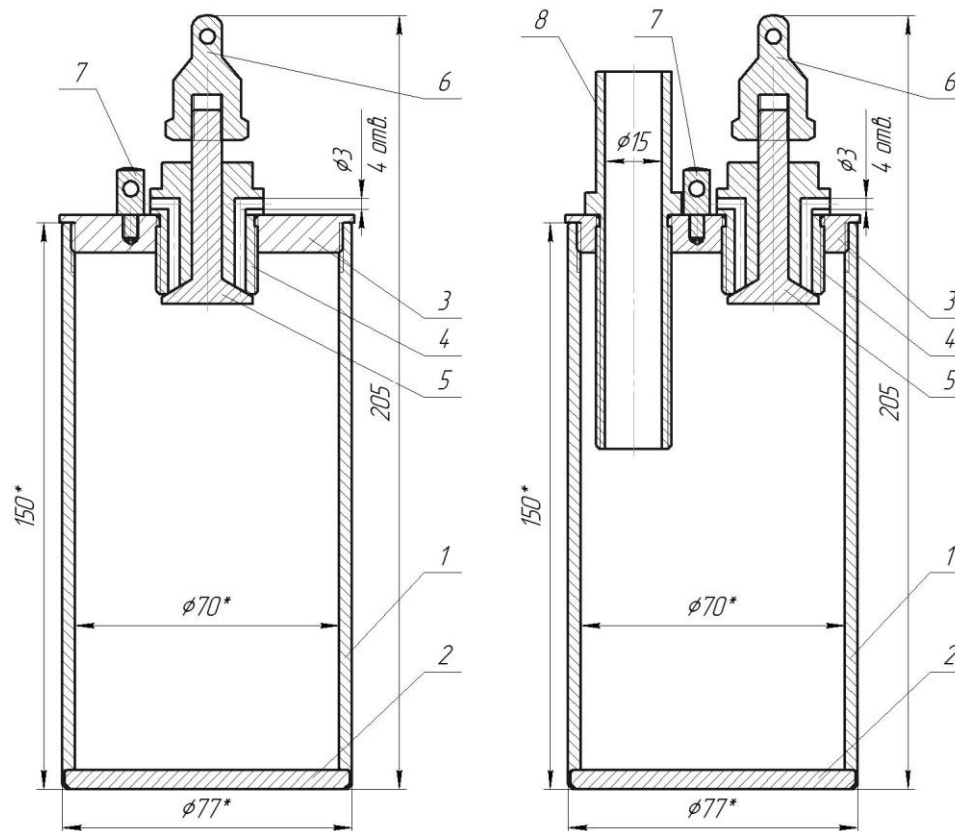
Эскиз пробоотборника типа ППС: 1 – стакан; 2 – донце; 3 – крышка; 4 – седло; 5 – клапан; 6 – упор; 7 – бабышка; 8 – трубка для термометра (опционально).
